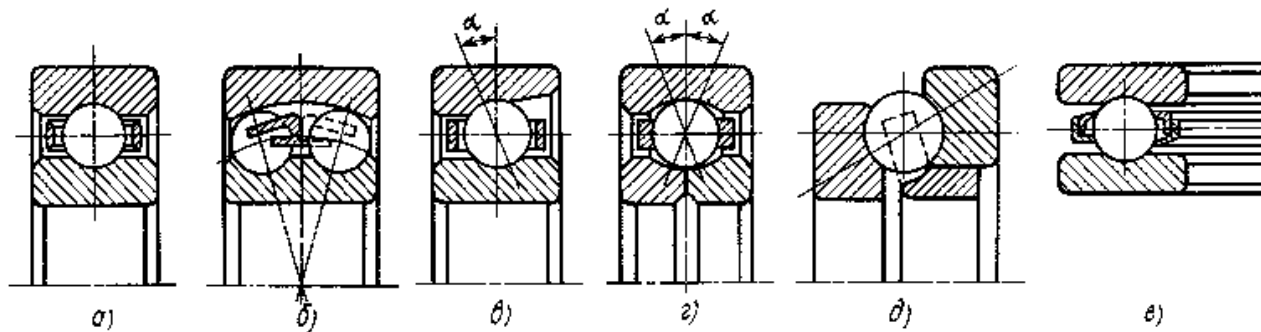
Основные типы шарикоподшипников: а – радиальные однорядные; б – двухрядные несамоустанавливающиеся; в, г – радиально-упорные; д – упорно-радиальные; е – упорные
